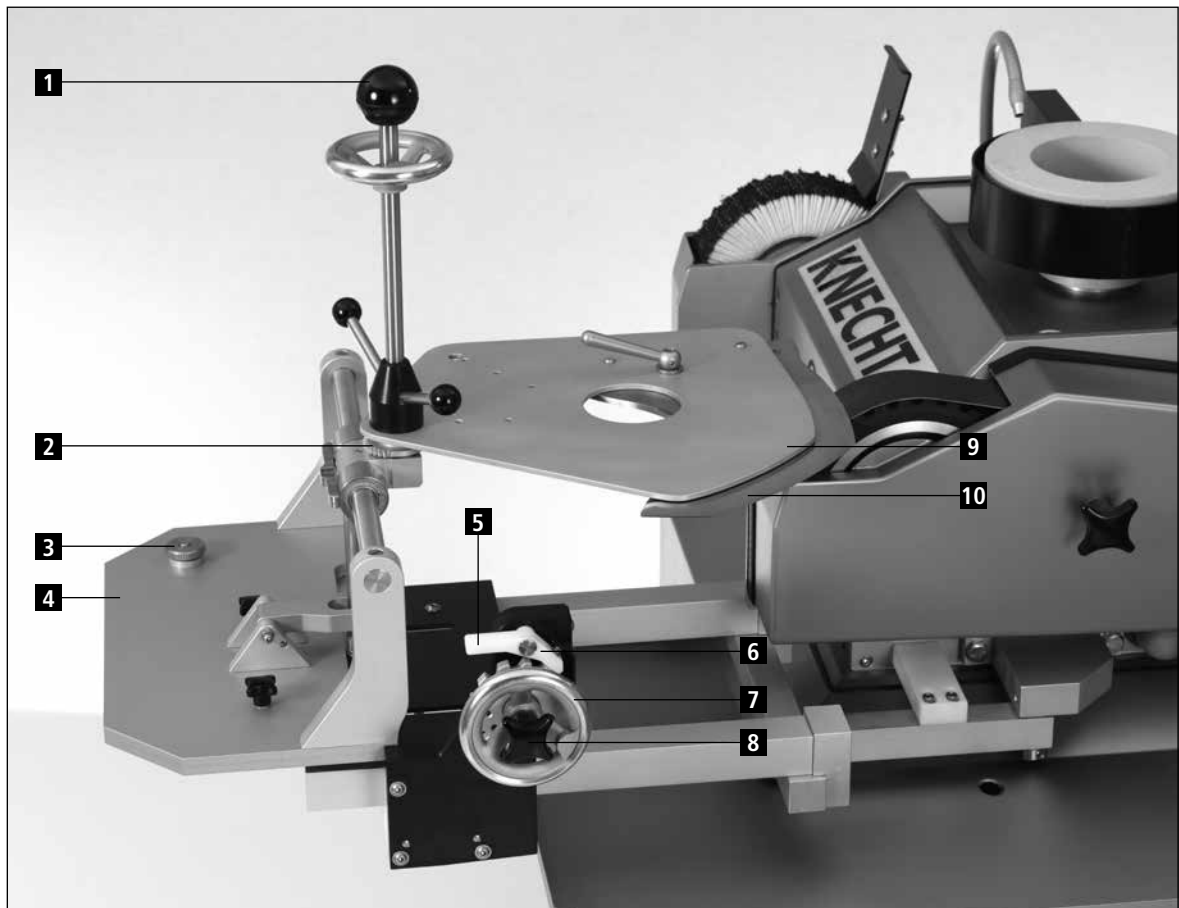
Vue d'ensemble du dispositif universel d'affûtage par bande
